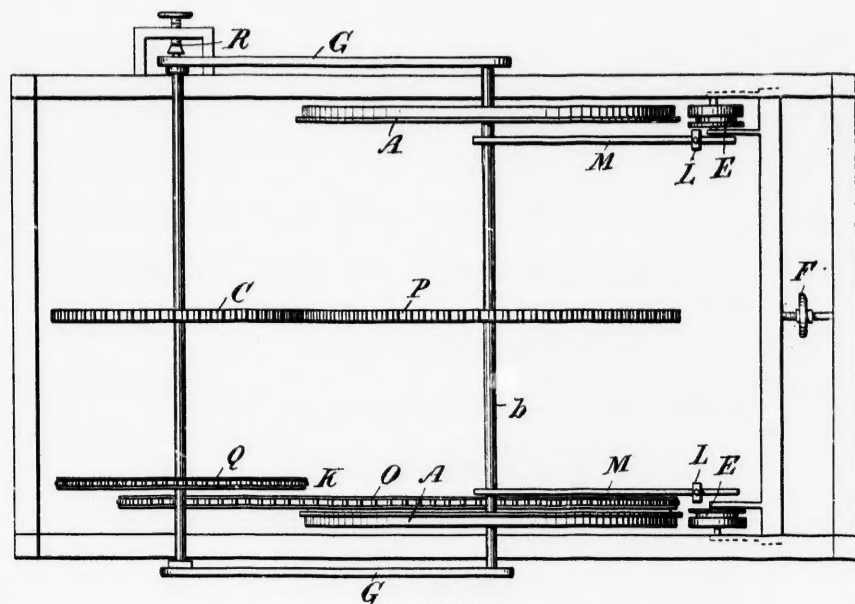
Le Moteur Centripète Horizontal vu d'en-dessus.
